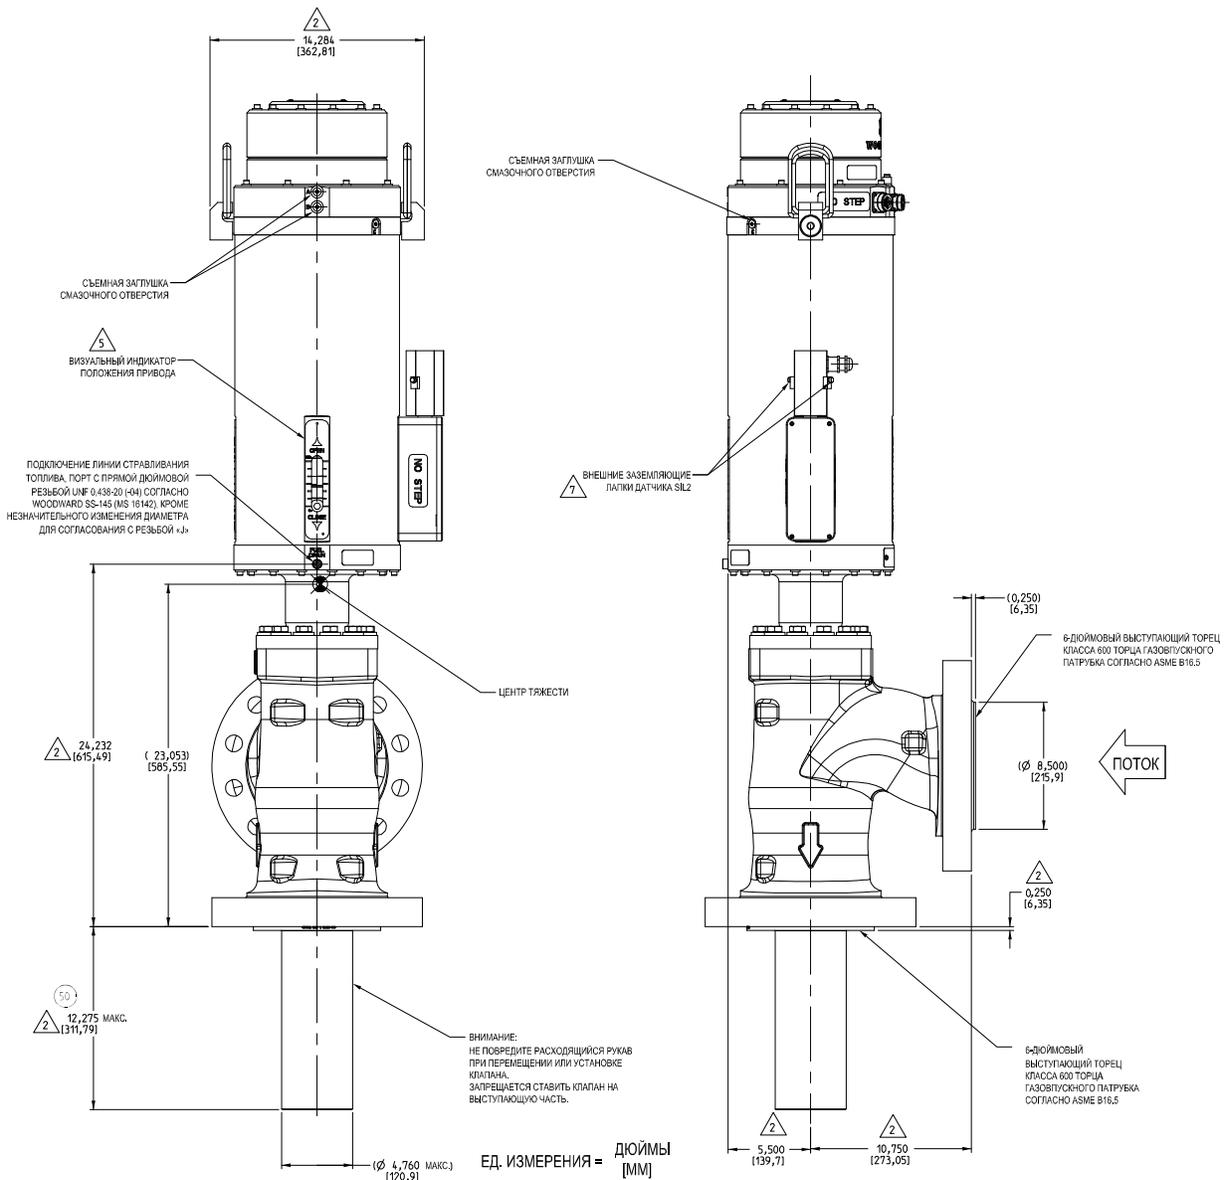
а. Габаритный чертеж (6-дюймовый клапан LESV II класса 600)
